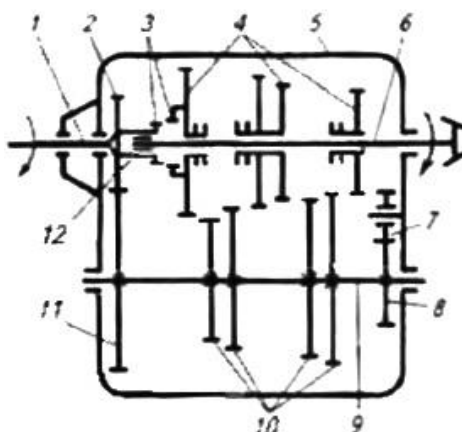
Кинематическая схема трехвальной коробки переключения передач (КПП) с прямой передачей:
